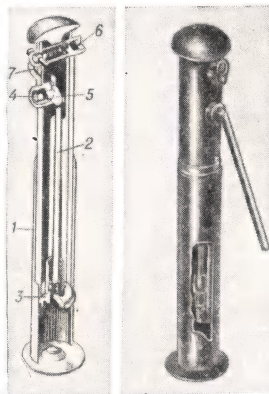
Гидравлическая стойка: 1 — корпус; 2 — выдвижная часть; 3 — диск с уплотнением; 4 — гнездо для рукоятки гидравлического насоса; 5 — кривошип; 6 — разгрузочный клапан; 7 — серьга разгрузочного клапана.
